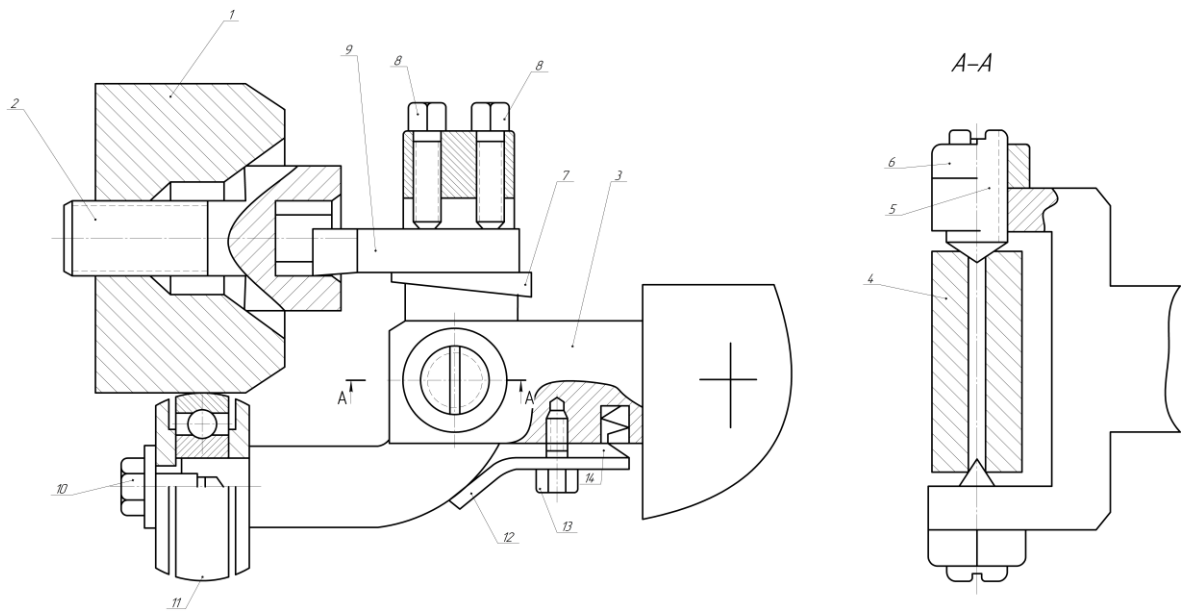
Пристрій для обробки фасонних поверхонь
